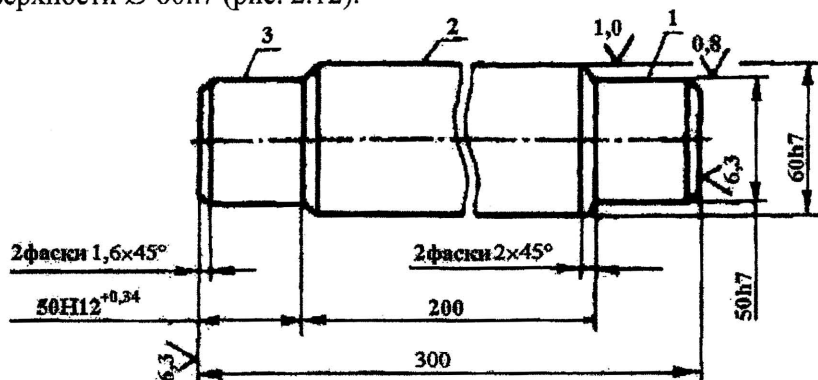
Заготовка – горячекатаный прокат обычной точности.
